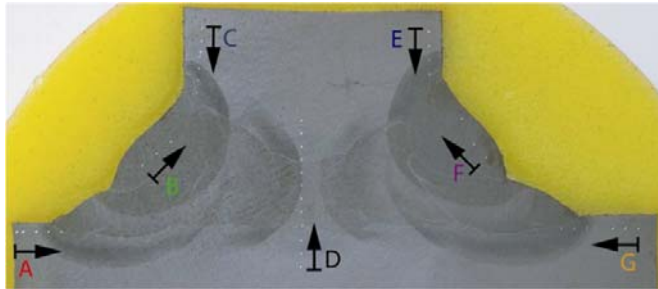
Schlibbild einer Kreuzstoßprobe
